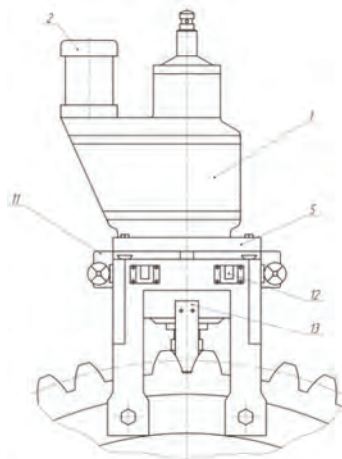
Приставной вертикальный зубофрезерный станок - вид сбоку
